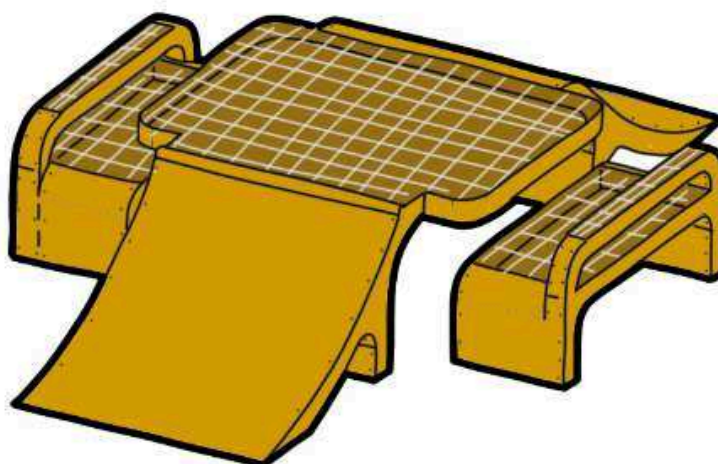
Ilustração de fabricação - Molde Madeira com malha de Aço.
